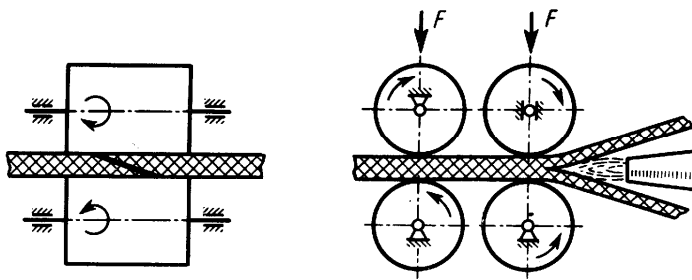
Сварка нагретым газом без присадочного материала
